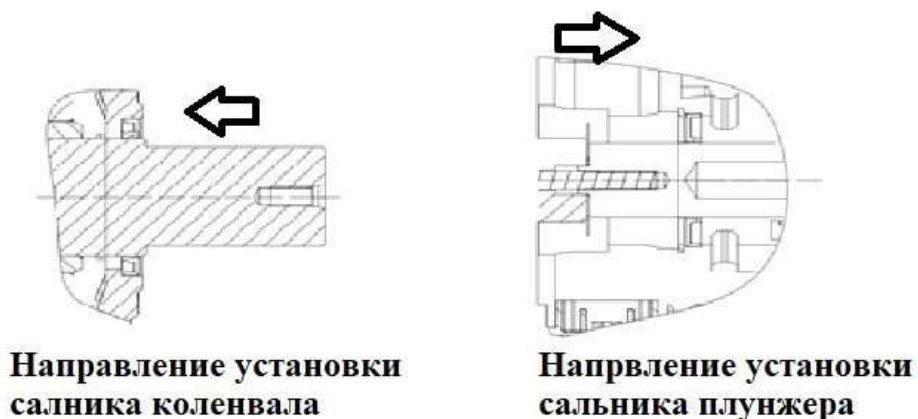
Направление установки сальника коленчатого вала и сальника плунжера
